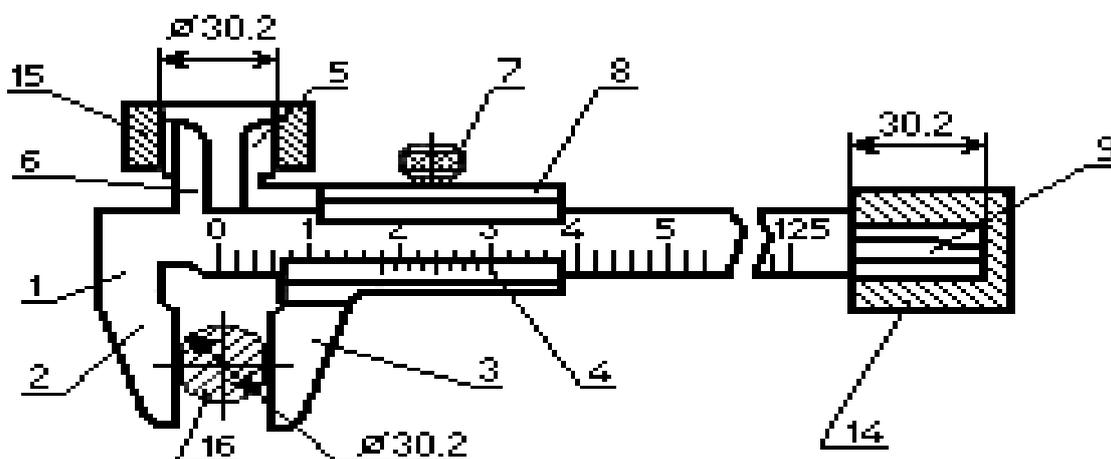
Измерение деталей штангенциркулем ШЦ-1
